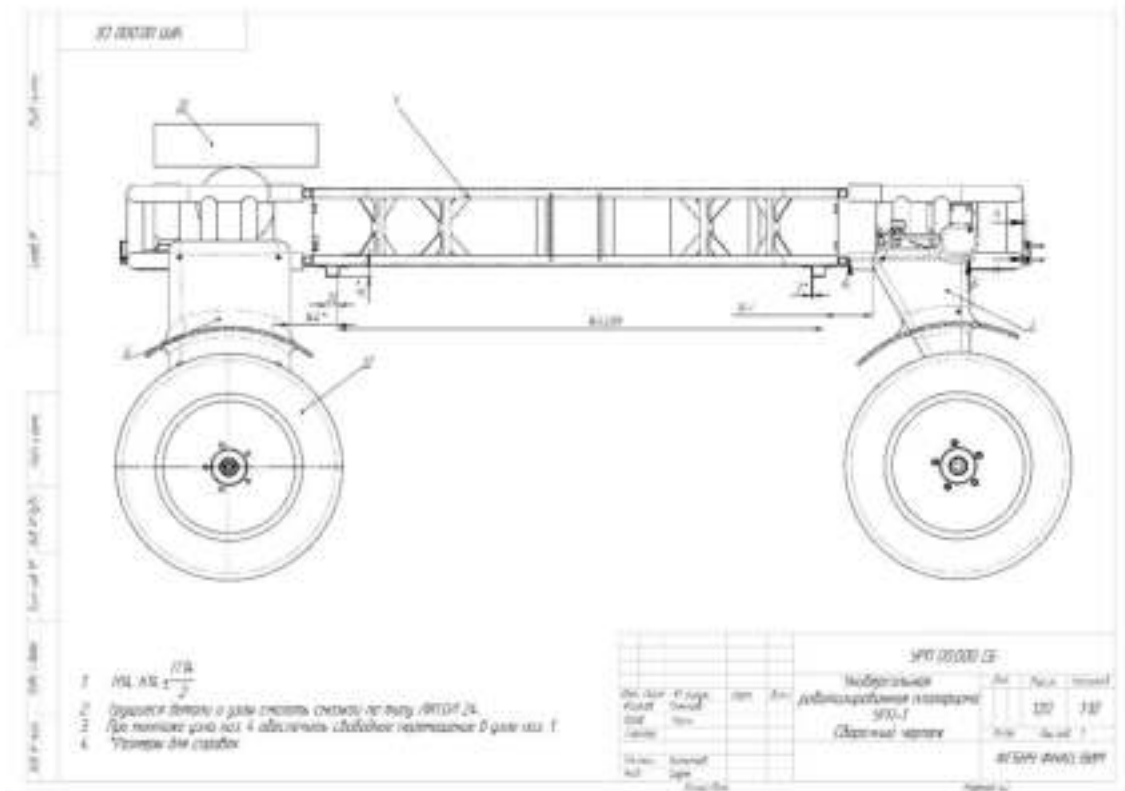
Сборочный чертёж УРП-1 (вид сбоку)
